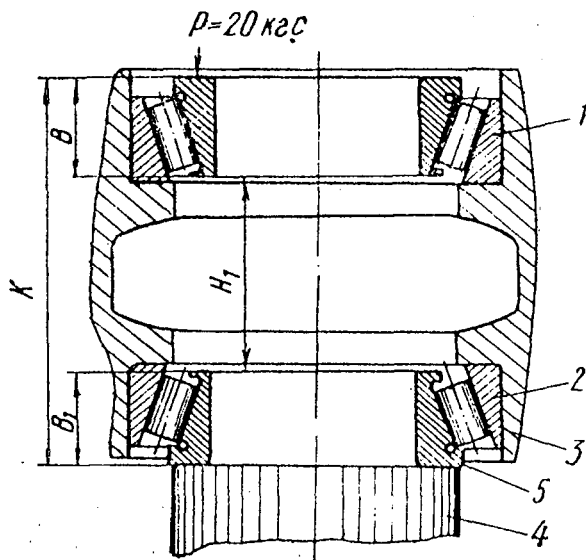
Схема замера зазоров в роликоподшипниках:
